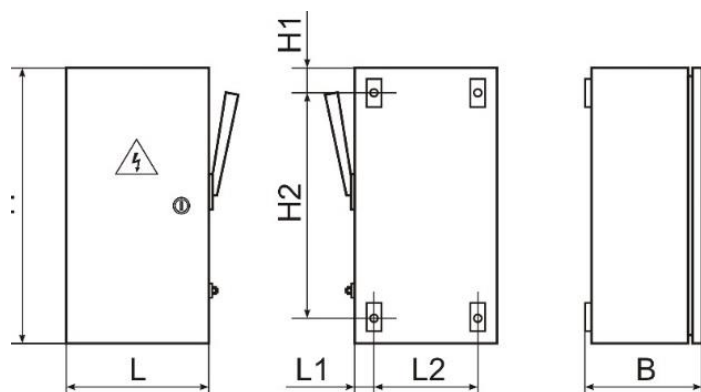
Общий вид и габаритные размеры ящиков силовых
